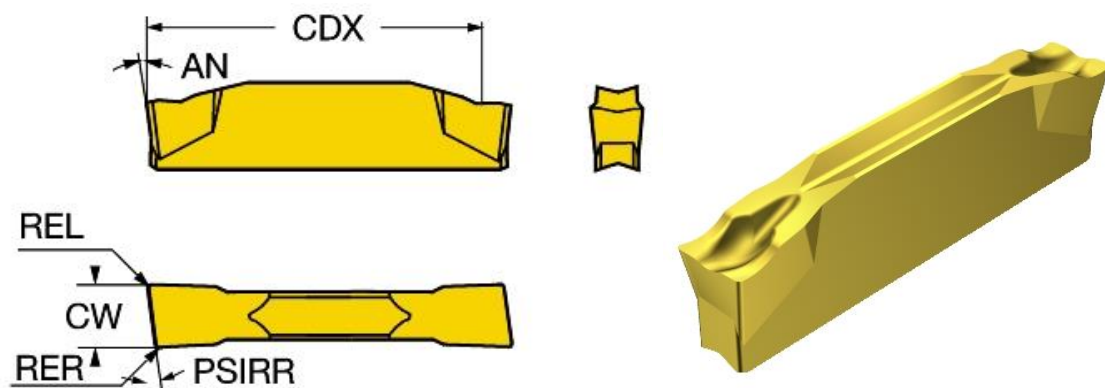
Зовнішній вигляд Пластина R123H2-0400-0502-СМ 2135
